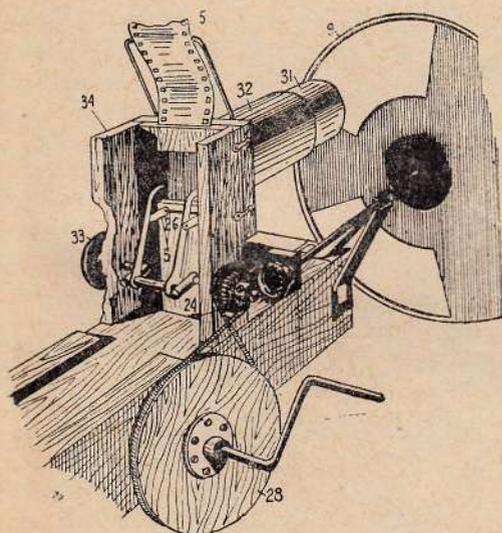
Механическая часть (вид сзади), 5 — пленка, 9 — обтюратор, 25-26 — коленчатый вал, 28 — большой шкив, 31 — внутренний тубус; 32 — наружный тубус, 33 — шкив, 34 — щетки
